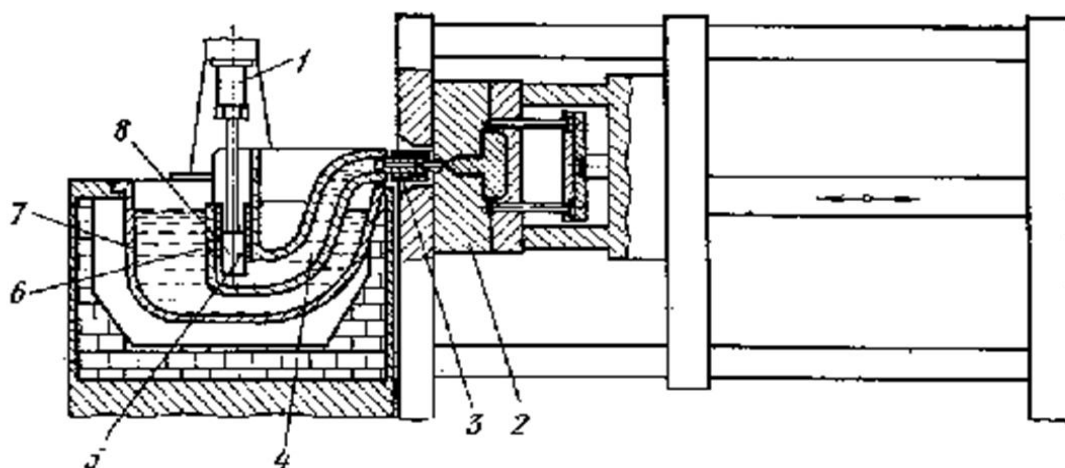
Литейная машина с горячей камерой прессования: 1 – цилиндр; 2 – пресс-форма; 3 – мундштук; 4 – канал; 5 – полость цилиндра; 6 - отверстие; 7 - чугунный тигель; 8 – поршень.
